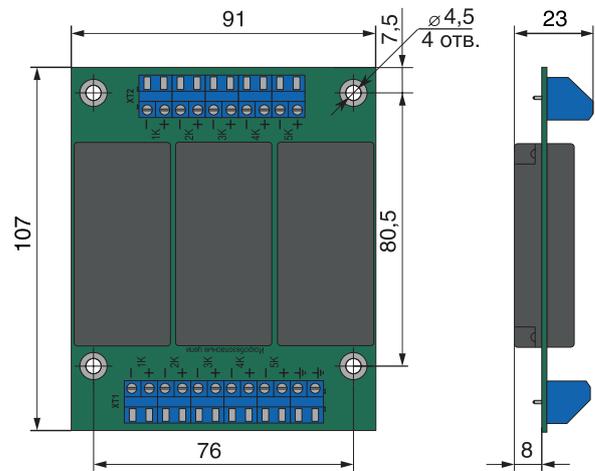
Габаритные размеры барьеров ЭНИ-БИС-112, 114-Ex-01
